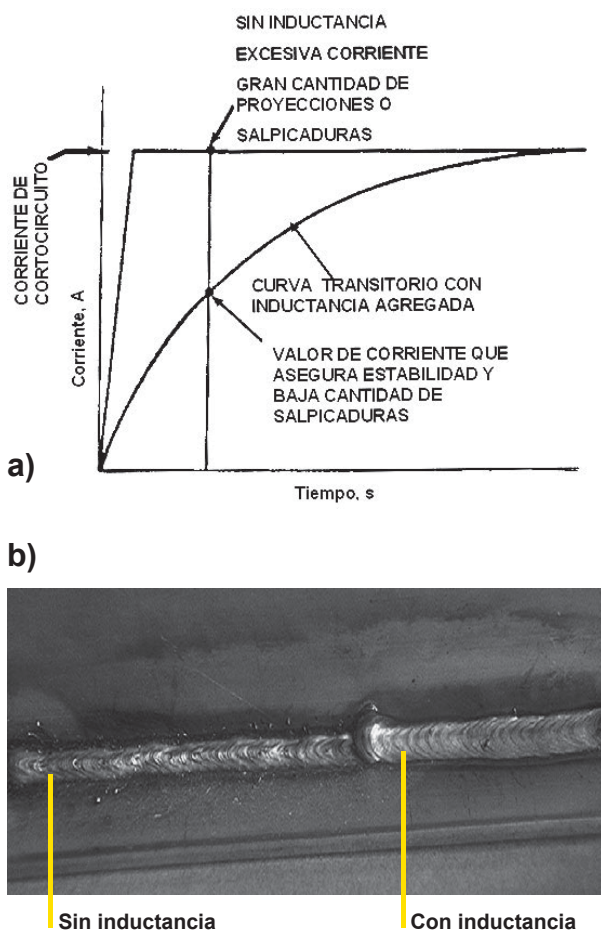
| Efecto de la inductancia en la soldadura MIG-MAG
